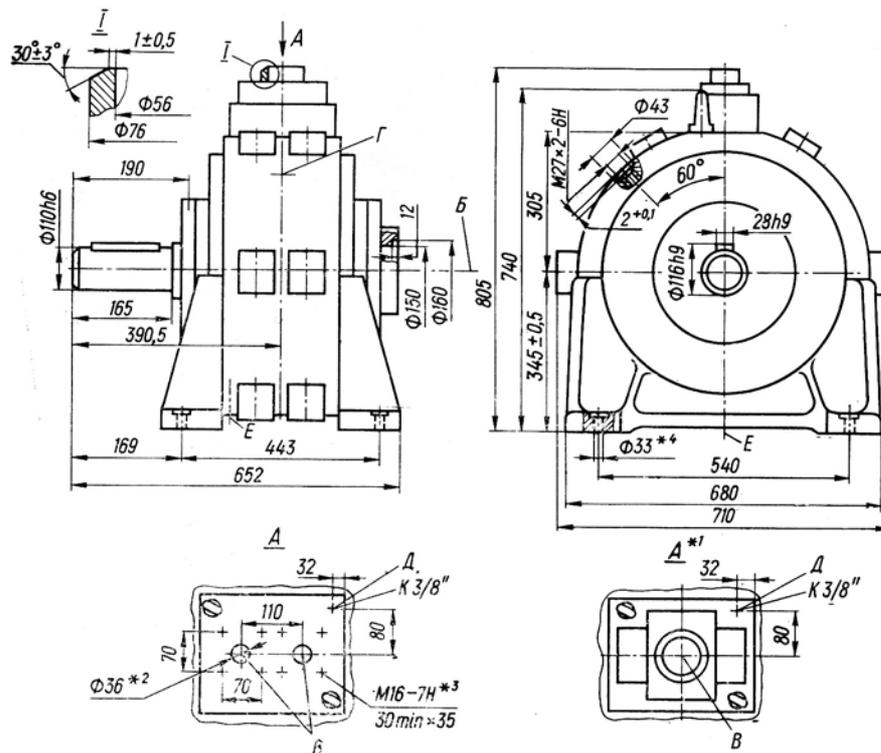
Основные габаритные и присоединительные размеры насосов типа HP2-710
